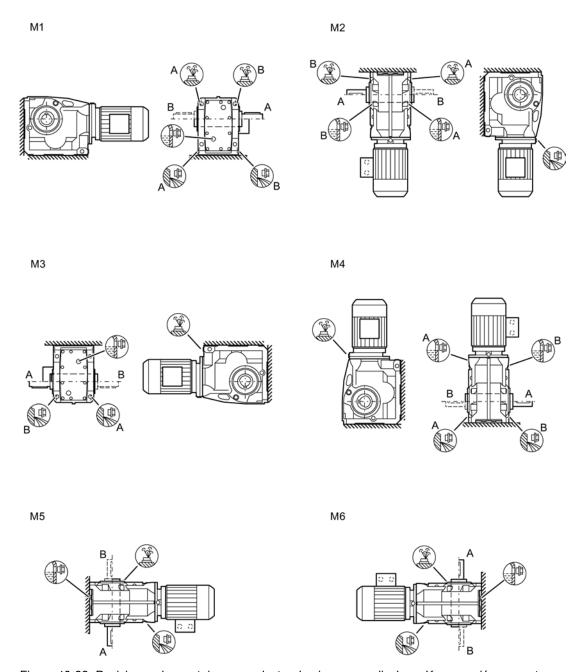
Posiciones de montaje para reductor de ejes perpendiculares K. en versión con patas, tamaños 39 - 149
